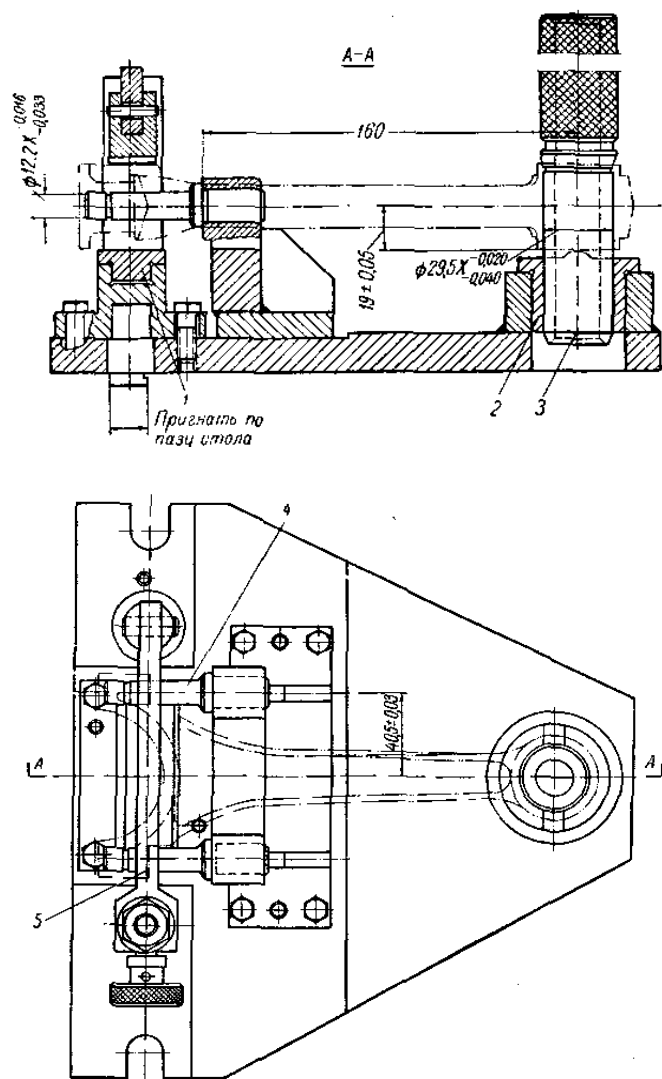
Приспособление для фрезерования торцов разъема нижней головки шатуна
